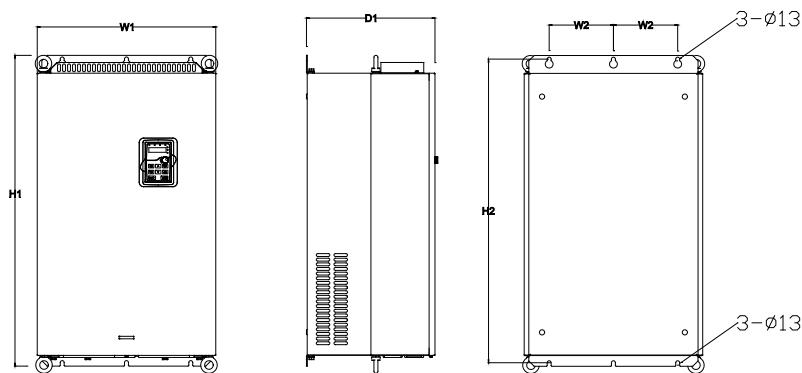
Настенный монтаж 132 – 200 кВт
